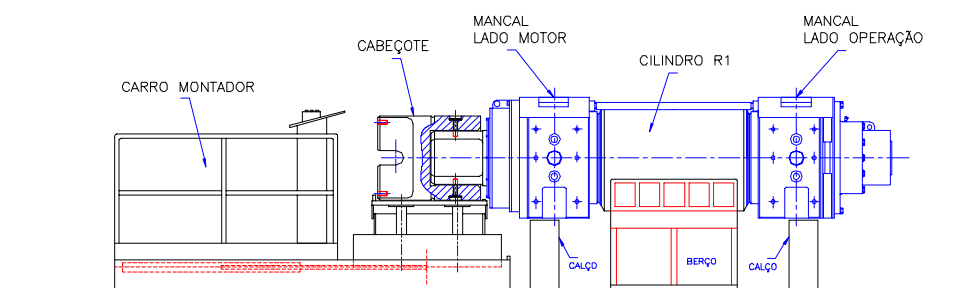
Dispositivo de montagem/desmontagem de cabeçotes (Montagem).
